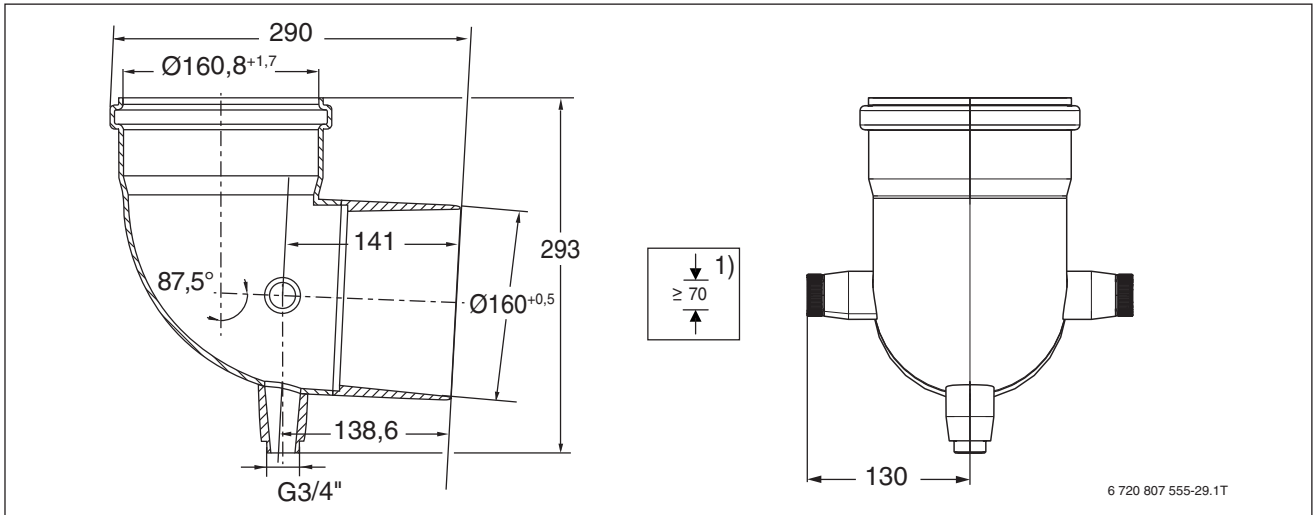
Anschlusswinkel 87° DN 160 (Maße in mm)
